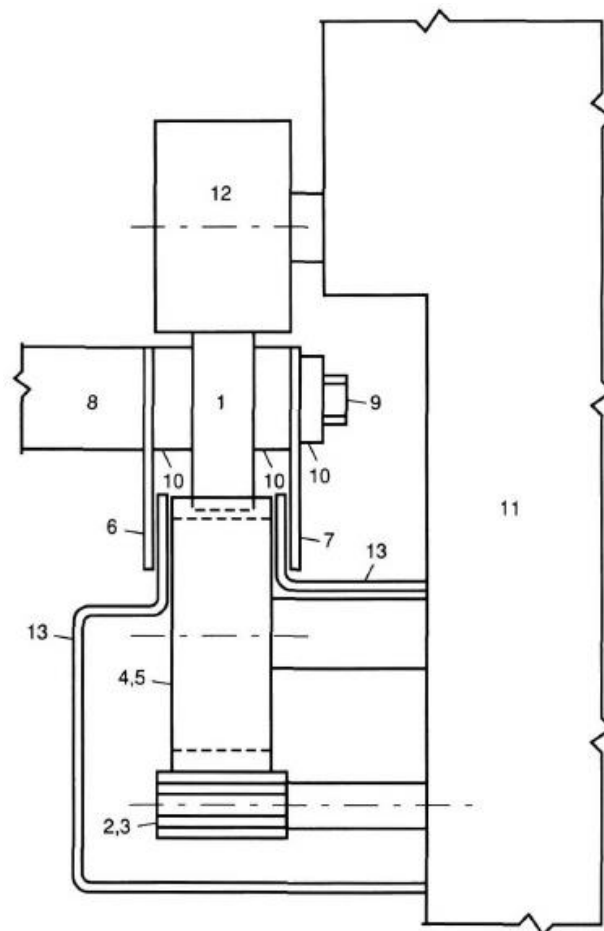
Vista lateral do mecanismo de rodas e engrenagens para locomoção de uma carruagem. Retirado de [5]
